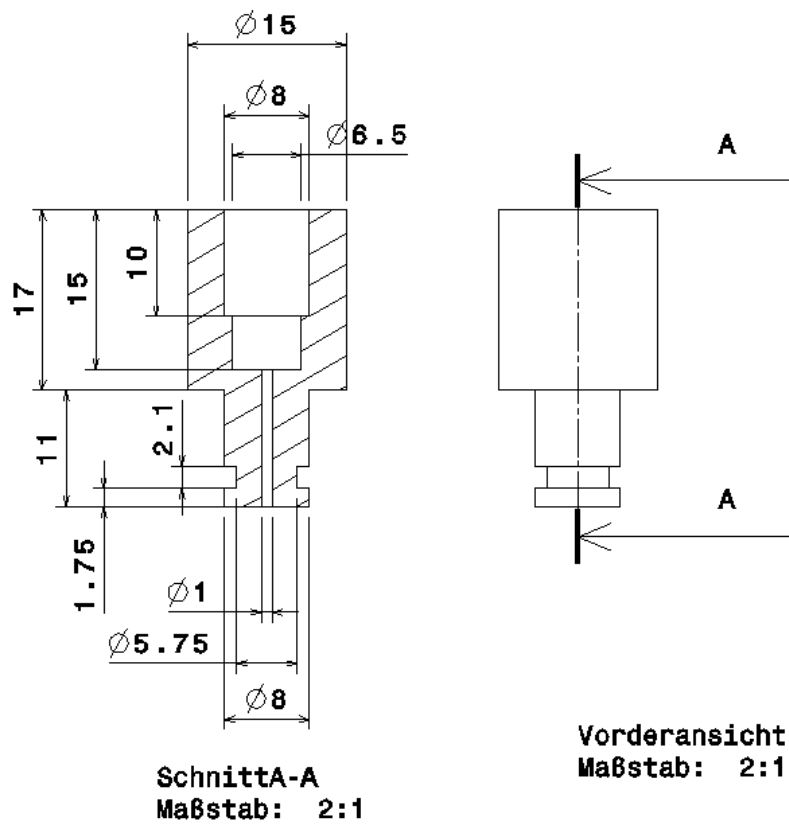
Konstruktionszeichnung Adapter zum Einkleben einer Kanüle mit Durchmesser 0.8 mm.
